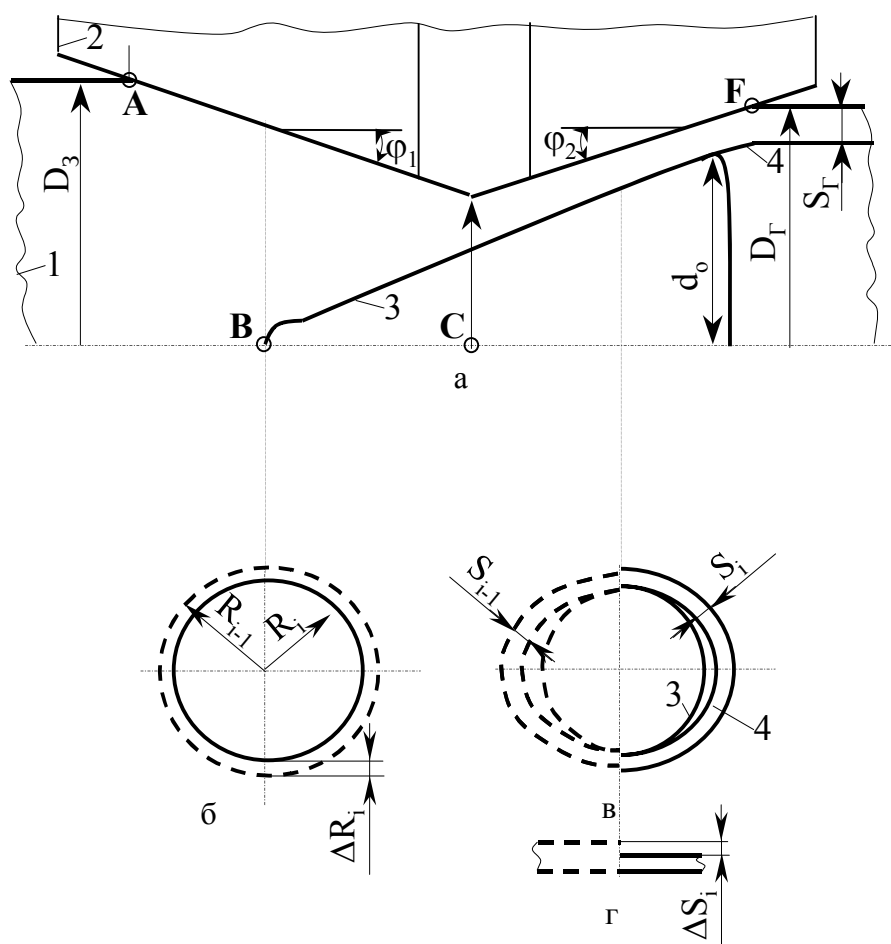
Схемы продольного сечения очага деформации при прошивке заготовок (а), а также поперечных сечений заготовки (б, сечение I) и гильзы (в, сечения II): г – развертка гильзы; 1 – заготовка; 2 – валок; 3 – оправка; 4 – гильза
